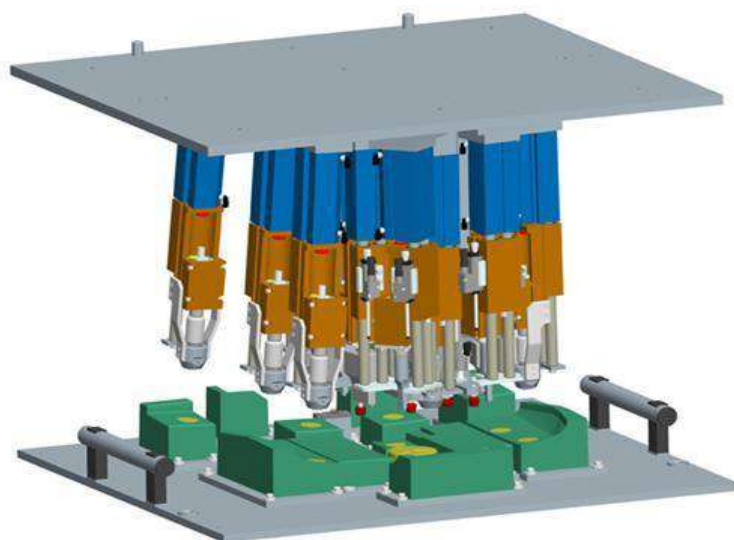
Багатоточковий автоматизований комплекс для ультразвукового зварювання фірми Herrmann Ultrasonic
